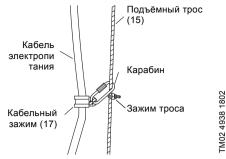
Крепление кабеля электропитания к подъёмному тросу
